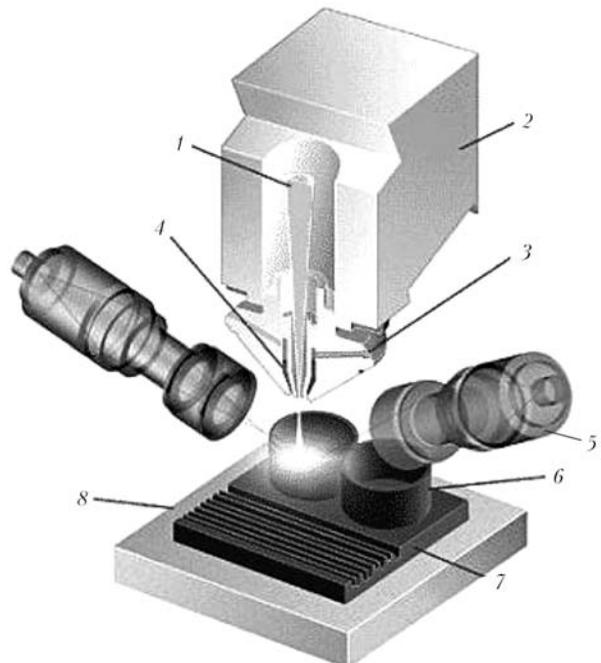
Схема процесса трехмерного синтеза изделий по DMD технологии: 1 — излучение CO₂-лазера; 2 — фокусирующая оптика; 3 — подача порошка; 4 — защитный газ; 5 — сенсоры оптической системы обратной связи; 6 — создаваемый объект; 7 — заготовка или форма; 8 — платформа
